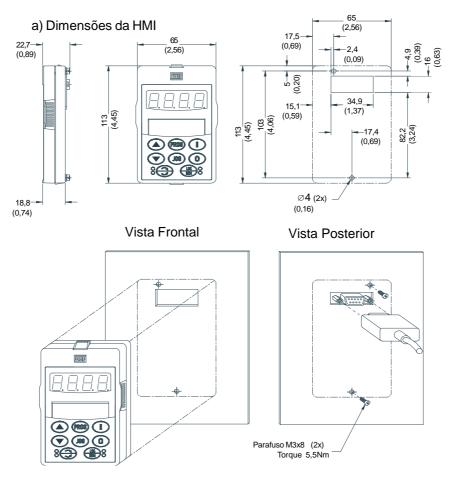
Dimensões da HMI em mm (in) e como instalar no painel sem moldura
